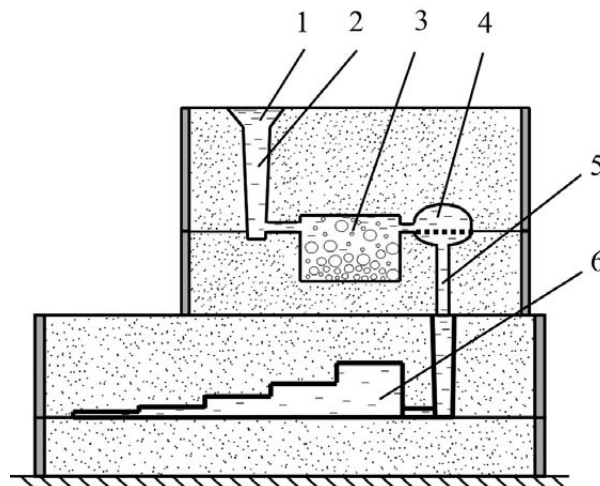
Схема ливарної форми для внутрішньо-формового сфероїдизуючого модифікування: 1 – ливникова воронка; 2 – стояк; 3 – реакційна камера; 4 – шлаковловлювач з сітчастим фільтром; 5 – зливний канал у нижню форму; 6 – ступінчаста проба.
